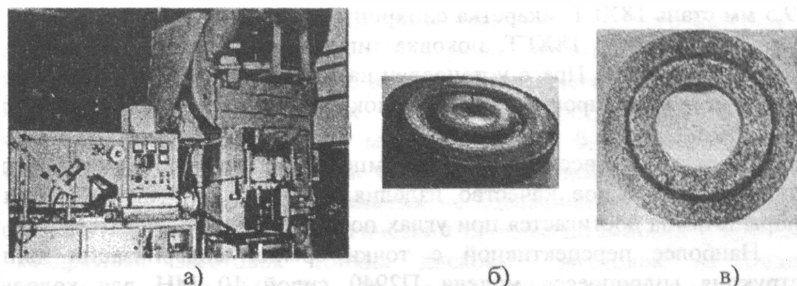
Внешний вид участка штамповки фрез (а) и поковок фрезы из стали Р6М5 (б) и «шайба коленвала» из стружковой заготовки (в)
